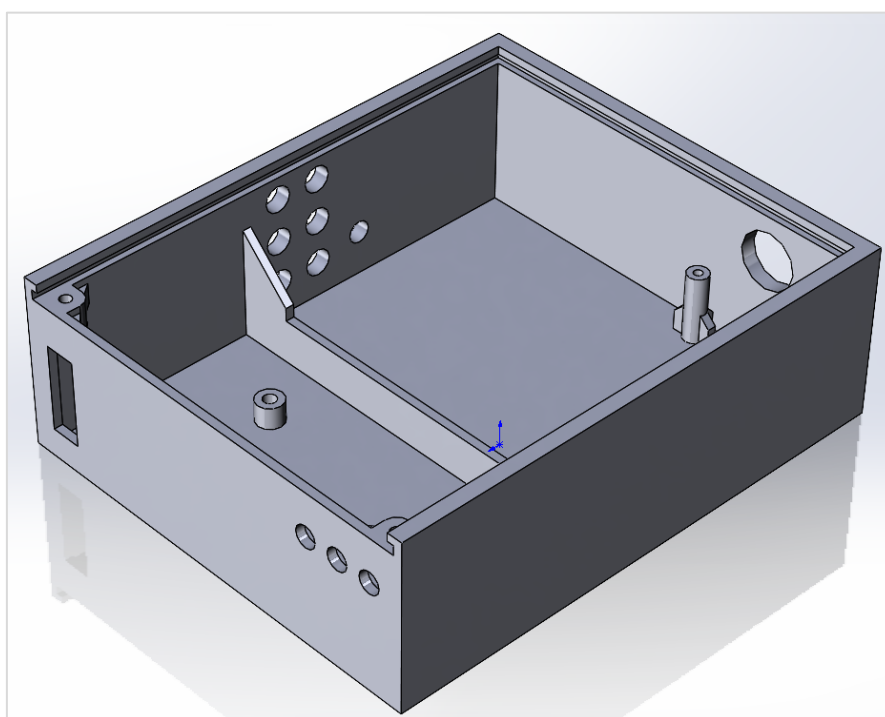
Общий вид нового корпуса, часть 2
